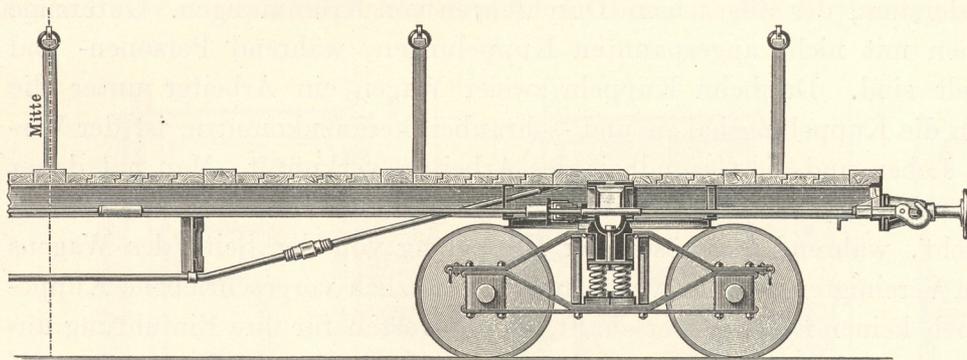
Plattformwagen (für lange Gegenstände) mit zwei vierrädrigen Drehgestellen.
